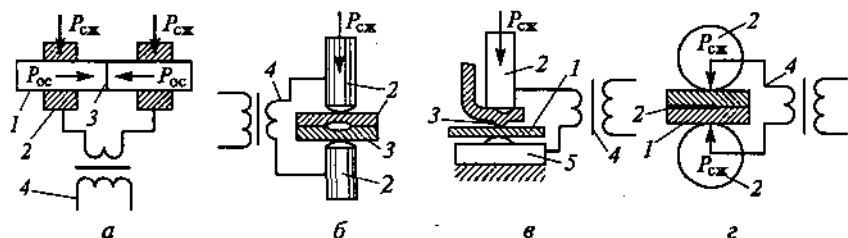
Виды контактной сварки: а — стыковая; б — точечная; в — рельефная; г — шовная; $P_{сж}$ — сила сжатия; $P_{ос}$ — осевое сжатие; 1 — свариваемое изделие; 2 — электроды; 3 — свариваемый шов; 4 — источник питания; 5 — контактная плита
